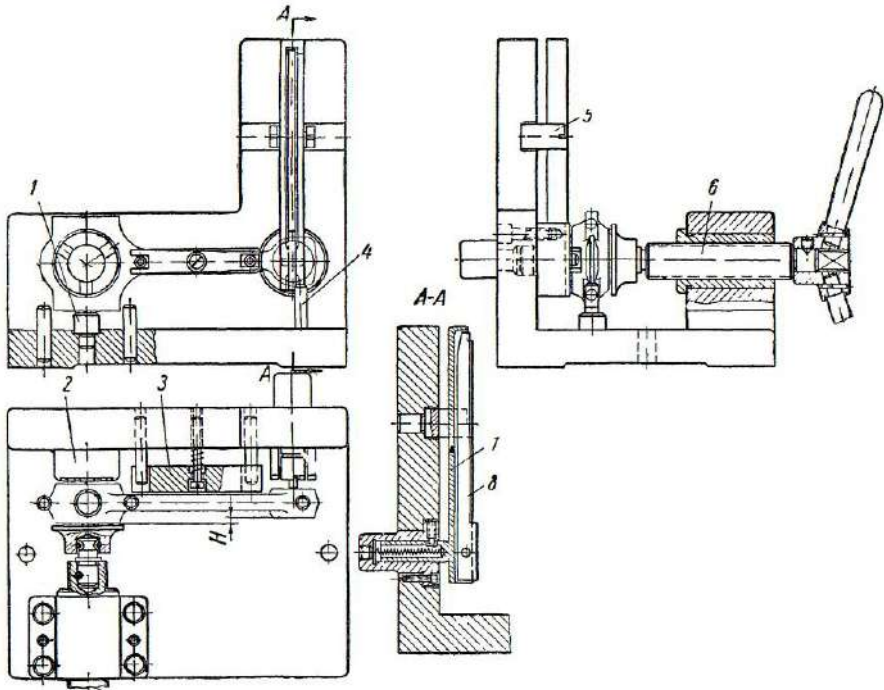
Пристосування для контролю заготовки шатуна
